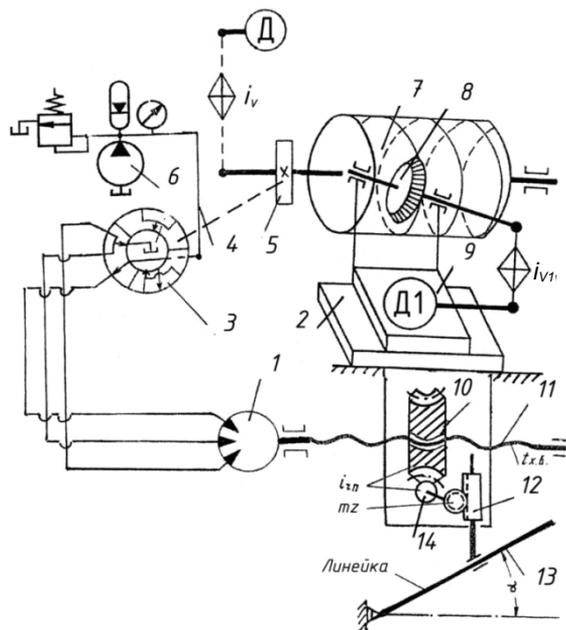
Структурная схема резбифрезерного станка с гидравлическими формообразующими связями для нарезания цилиндрических винтовых поверхностей переменного шага
